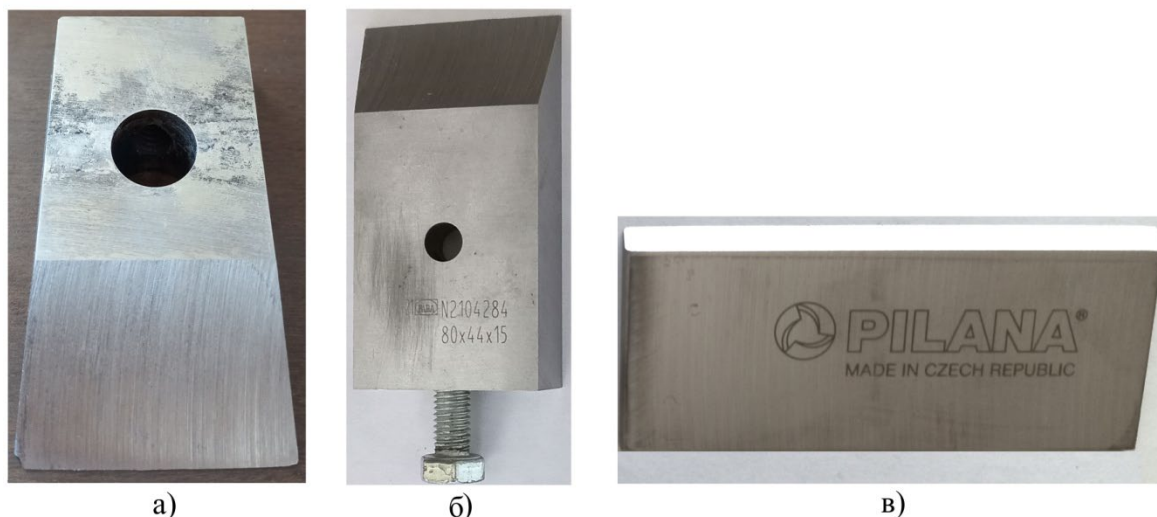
Виды ножей дереворежущего фрезерного инструмента: рубительные из сталей марок 6ХС (а) и “Faba” (б) и строгальные из стали марки “PILANA” (Чехия) (в).
